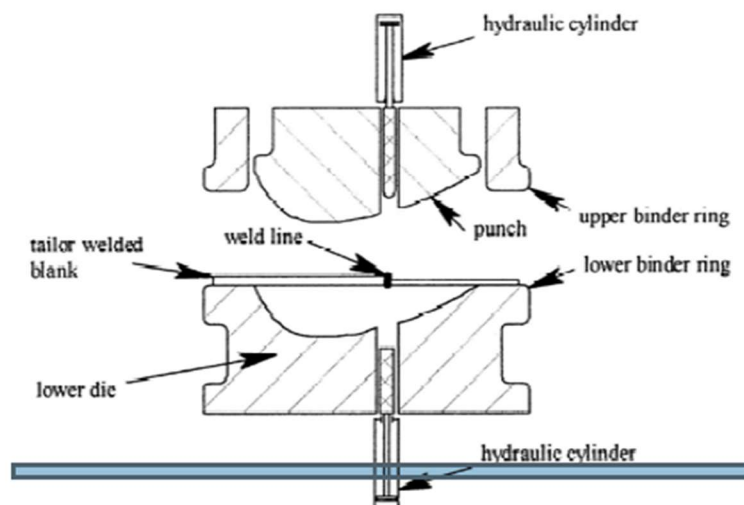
Схема комбинированного штампа для деформации гибридных заготовок. Гидравлические цилиндры обеспечивают минимальное
